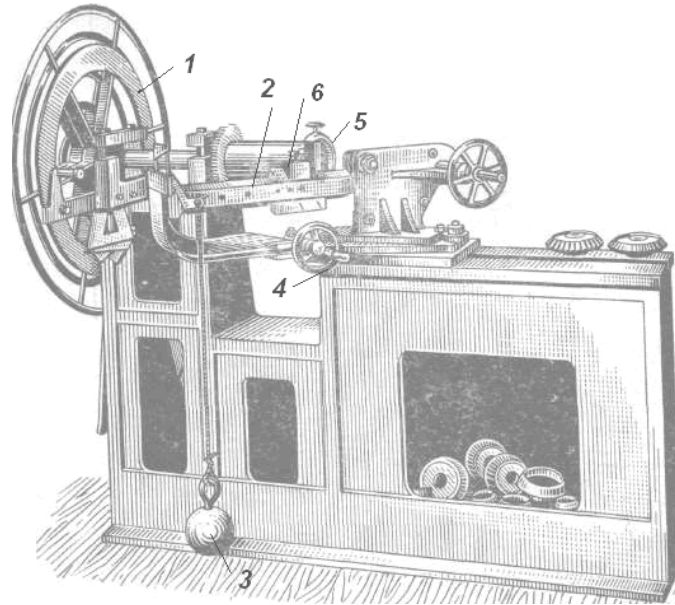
Зубострогальный станок для нарезания зубьев конических колес (конструктор Г. Модсли, первая четверть 19 в.):
